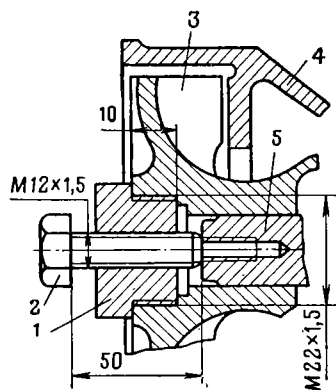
Установка съемника для спрессовки крыльчатки водяного насоса:
